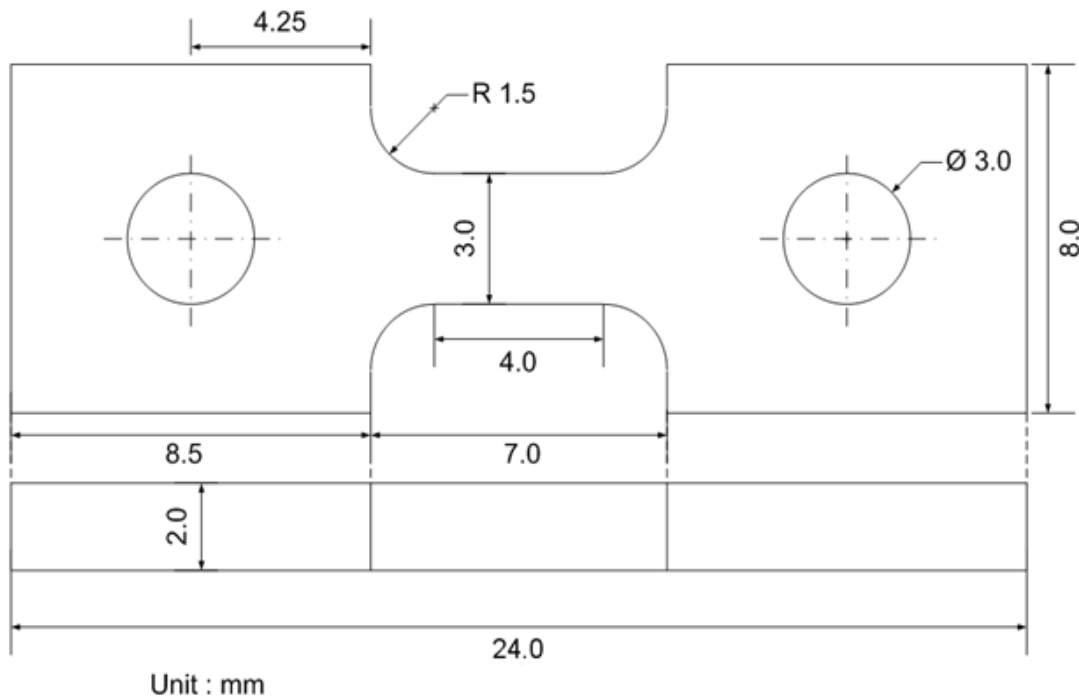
Desenho técnico do corpo de prova do ensaio de tração.
